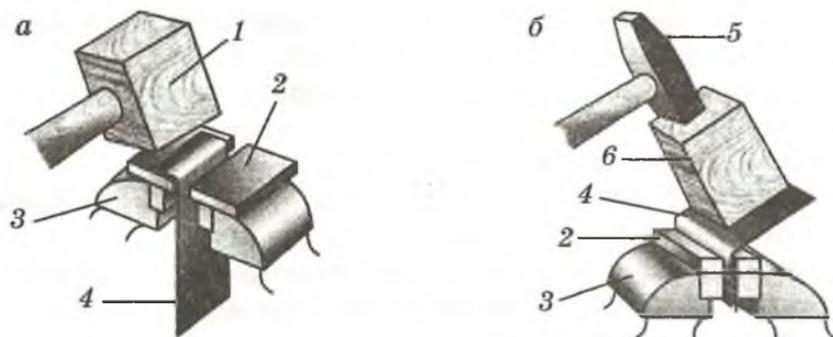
Гибка тонколистового металла в слесарных тисках: а — киянкой; б — слесарным молотком: 1 — киянка, 2 — нагубники, 3 — слесарные тиски, 4 — заготовка, 5 — слесарный молоток, 6 — деревянный брусок
